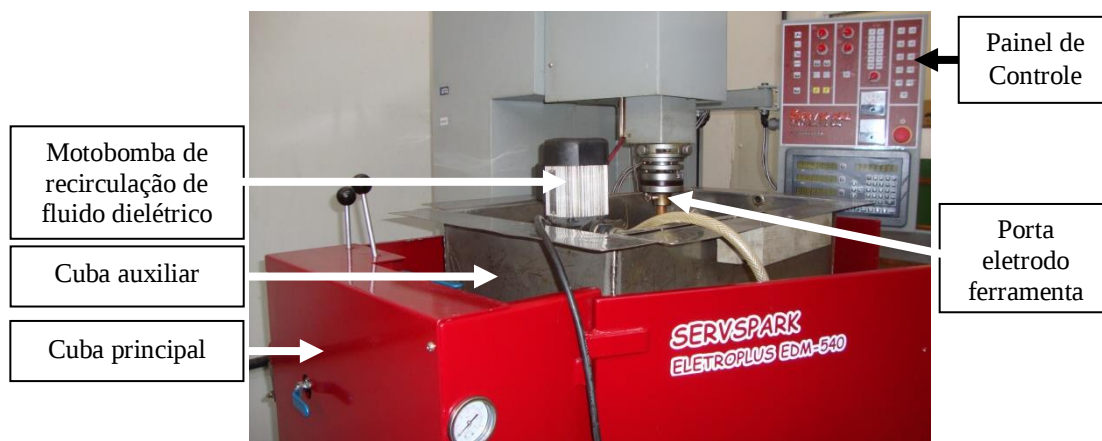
Cuba auxiliar instalada dentro da cuba principal da máquina EDM.
